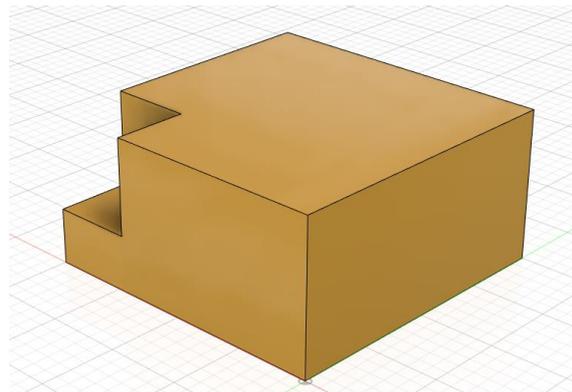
Fertige Form nach der Anwendung des Werkzeuges kombinieren
